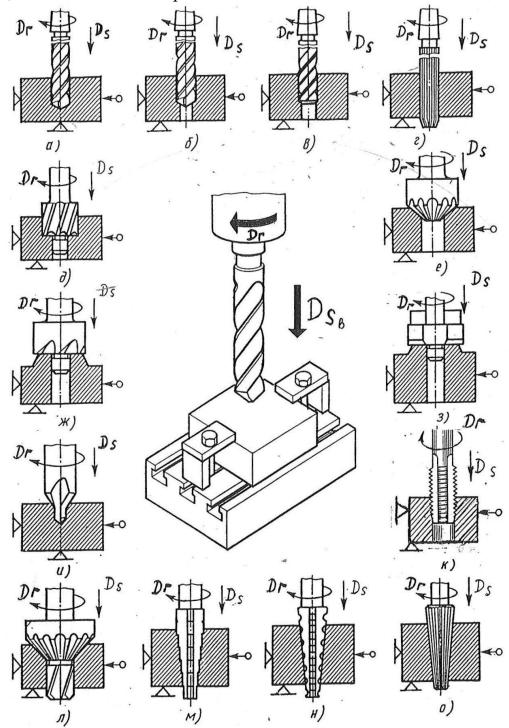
Схемы работы на сверлильных станках: а — сверление; б — рассверливание; в — зенкерование; г — развёртывание; д, е — зенкование; ж, з — цекование; и — центровка отверстия; к — нарезание резьбы; л — обработка комбинированным инструментом; м, н, о — развертывание конического отверстия
